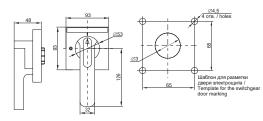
Габаритные размеры устройства, установленного на МССВ / Figure 2 - Overall dimensions of the device mounted on MCCB
